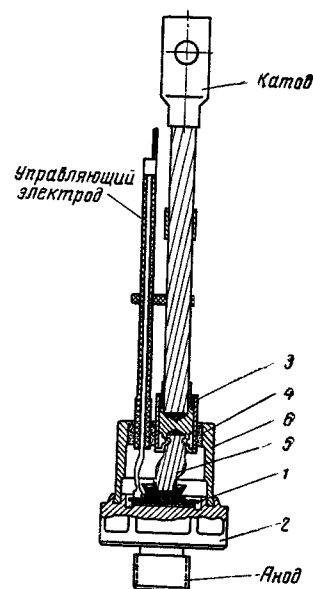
ВКУ-20 без радиатора: 1 — четырехслойный переход типа р-п-р-п; 2 — основание вентиля; 3 — втулка; 4 — стеклянный изолятор; 5 — гибкий вывод; 6 — корпус крышки.
